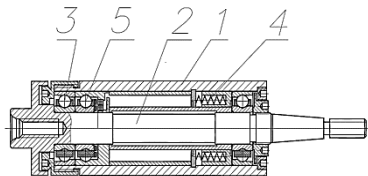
Пример конструкции шпиндельного узла с использованием разработанной конструкции мехатронного подшипника:
